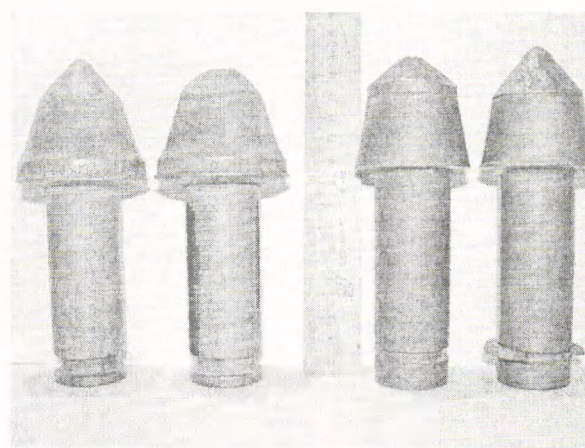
Вид изношенных резцов марки «Кеннаметал» (слева) и марки РЕМ 33-87-70/16М (справа)
